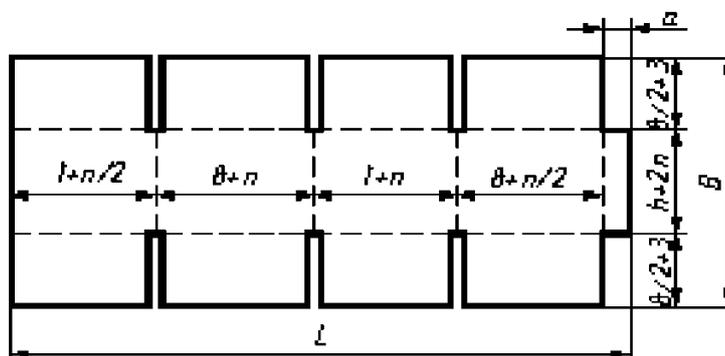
Развёртка заготовки ящика (исполнение А)
